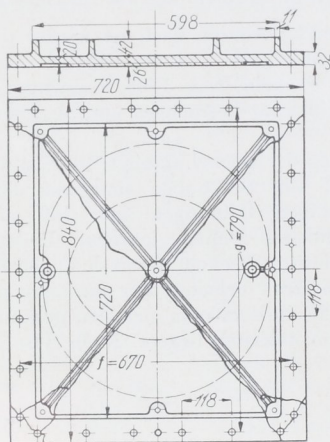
Bruch des Schieberkastendeckels des Dampfers Main. Nach Bach. M. 1:15.
